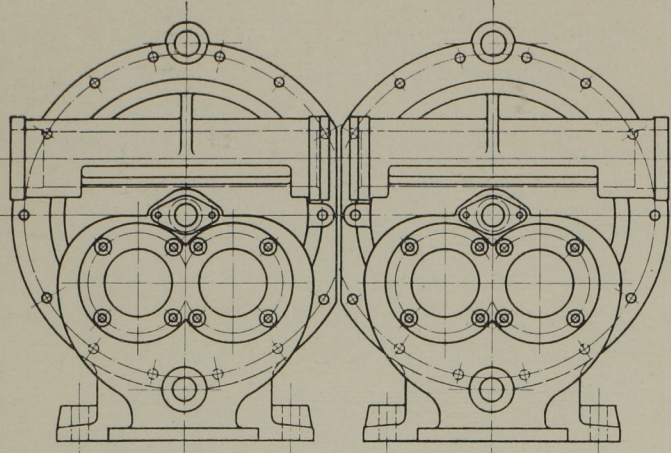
Rückansicht des Kompressors. Masst. 1:15.
